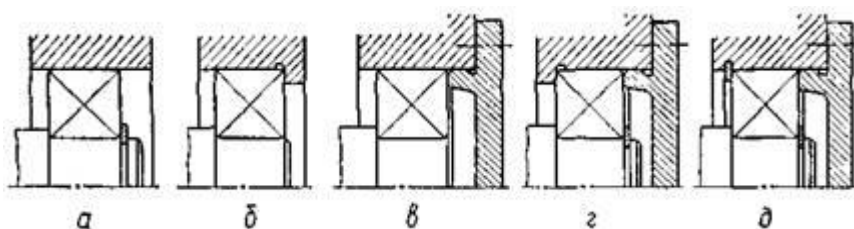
Монтаж підшипників у нерухомому корпусі
